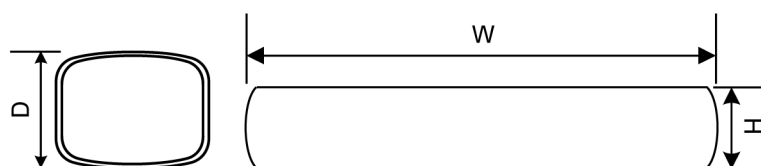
Representación esquemática, dimensiones en milímetros
